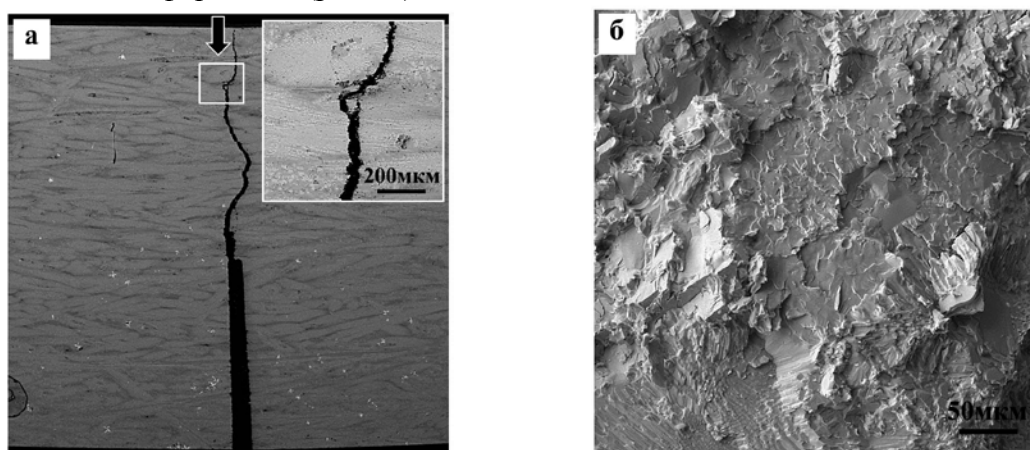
Разрушенный образец сплава системы Nb-Si-X после испытаний на трещиностойкость: (а) вид поверхности образца – исходный надрез с макротрещиной (стрелкой черного цвета показано направление приложения нагрузки) и (б) поверхность разрушения.
